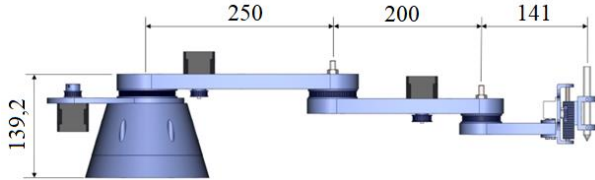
Çizim Robotu patlatma resmi (Explosion picture of the Drawing Robot)
